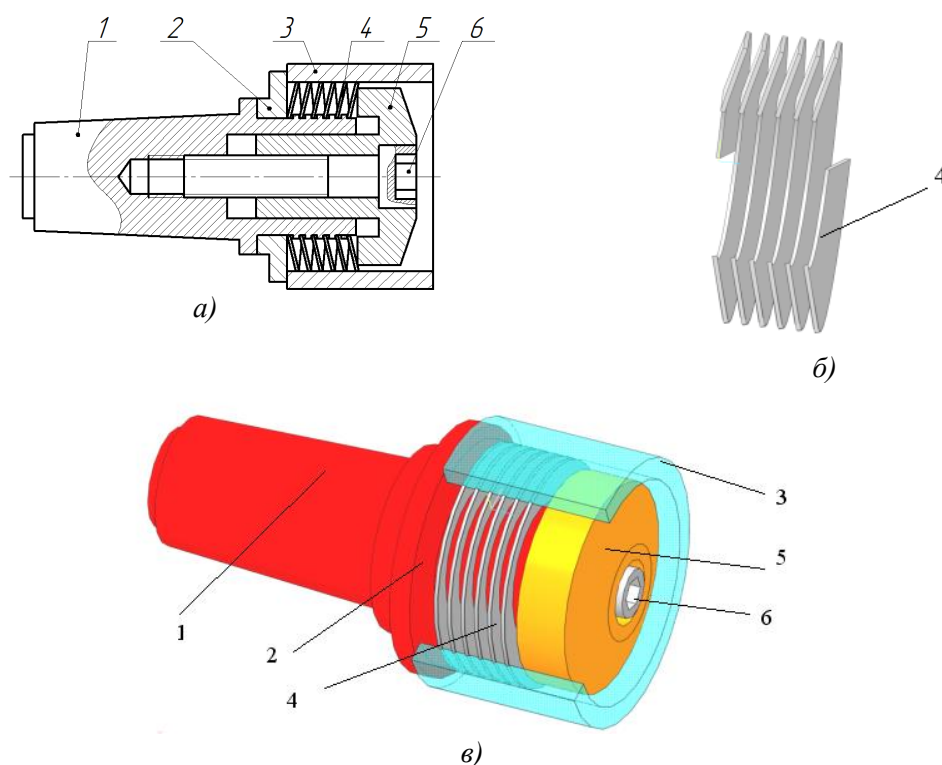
Конструкція оправки з пружними гвинтовими затискними елементами
